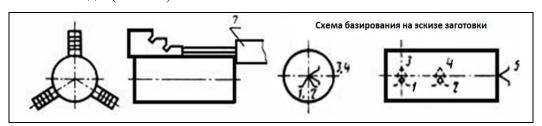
Установка заготовки по наружной цилиндрической поверхности и торцу в трехкулачковом патроне
